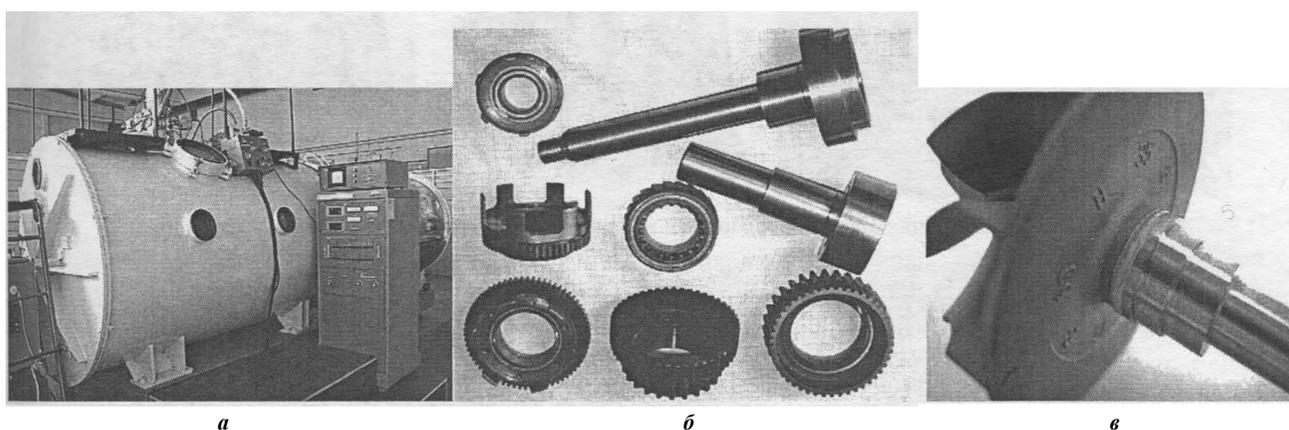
Комплекс оборудования ЭЛО (а), изготовленные с использованием ЭЛС шестерни и валы (б) и ротор турбокомпрессора (в)
